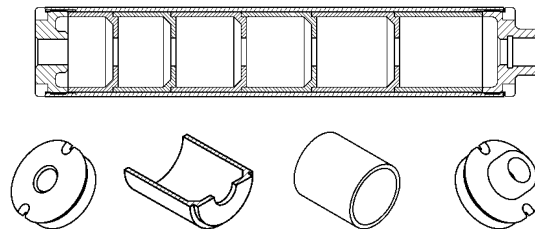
Схема прибора и внешний вид элементов рассекателя
